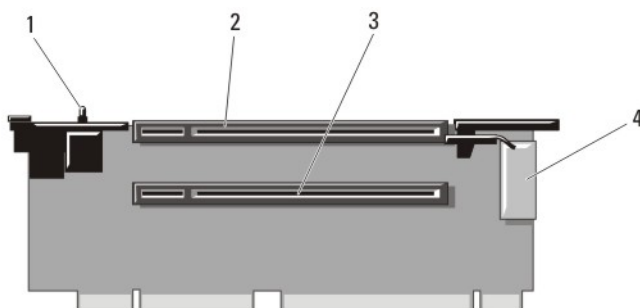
Identification des connecteurs de la carte de montage pour carte d'extension 2
